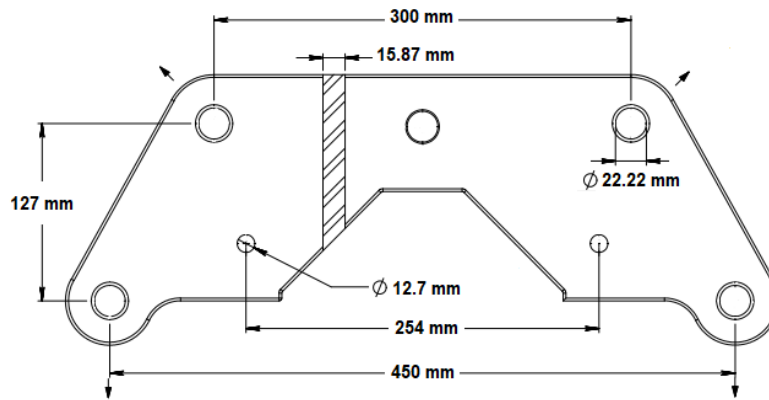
Detalle y dimensiones Yugo Trapezoidal
